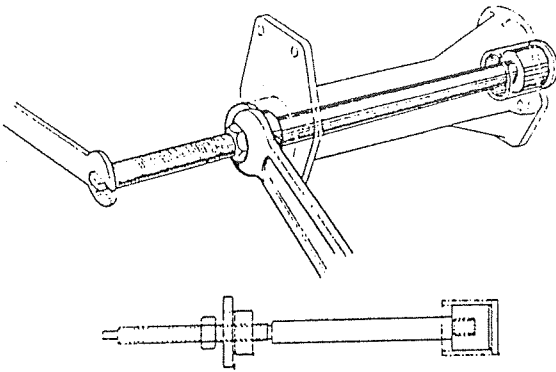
Montering av inre bussning i bakre lagerhylsa.
